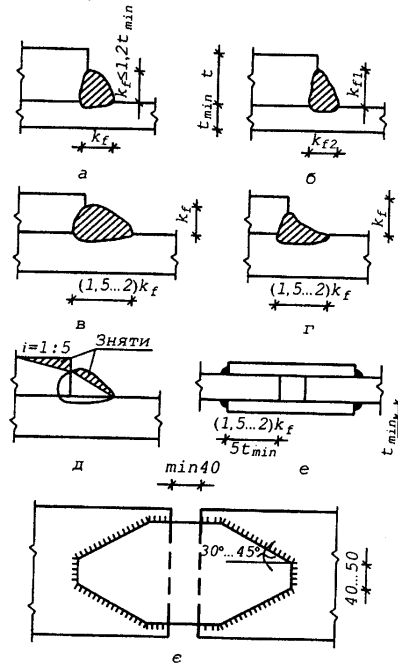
Конструювання з'єднань на кутових швах:
